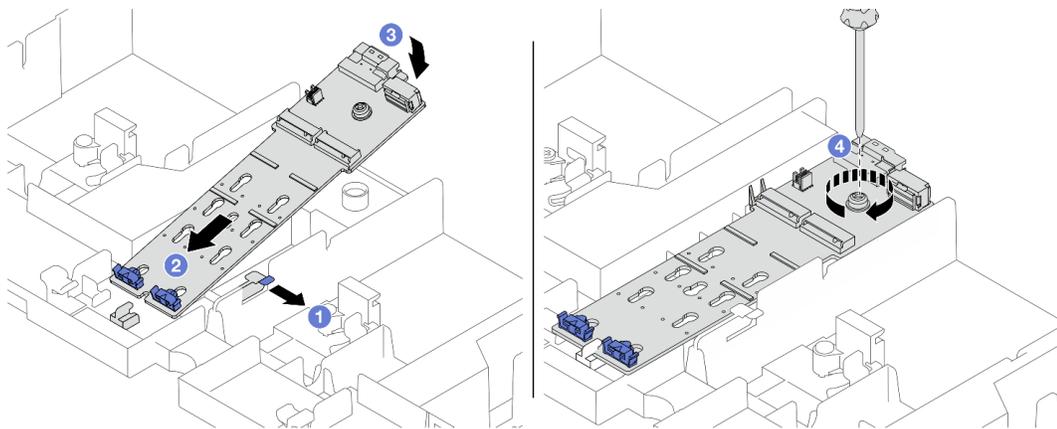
Installation du fond de panier M.2 sur la grille d'aération
